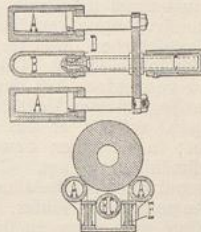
A Rücklaufbremse. B Ausrennzylinder. C Einrennzylinder. D Rückschlagventil. E Schlittenbalken.
